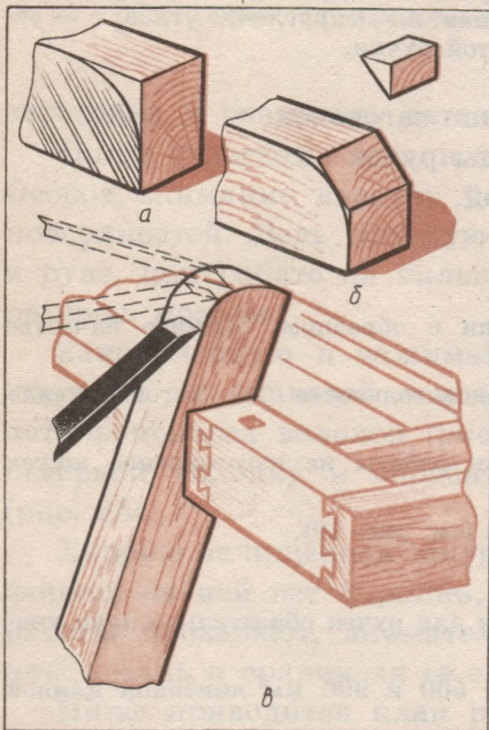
Скругление углов боковых стенок кузова носилок: а — разметка по шаблону; б — отпиливание углов; в — скругление углов.
